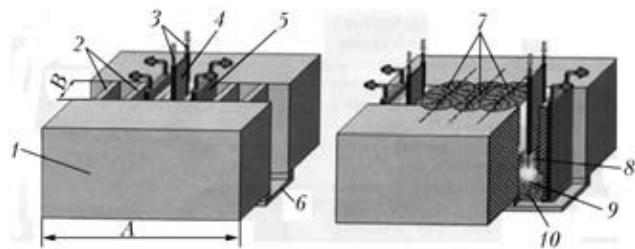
Схема многопроходной электрошлаковой сварки: 1 — свариваемая деталь; 2 — формирующие вставки; 3 — электродные проволоки; 4 — плавящийся мунштук; 5 — водоохлаждаемое устройство; 6 — входной карман; 7 — сварные швы; 8 — шлаковая ванна; 9 — металлическая ванна; 10 — наплавленный металл; А — толщина свариваемого металла; В — сварочный зазор
